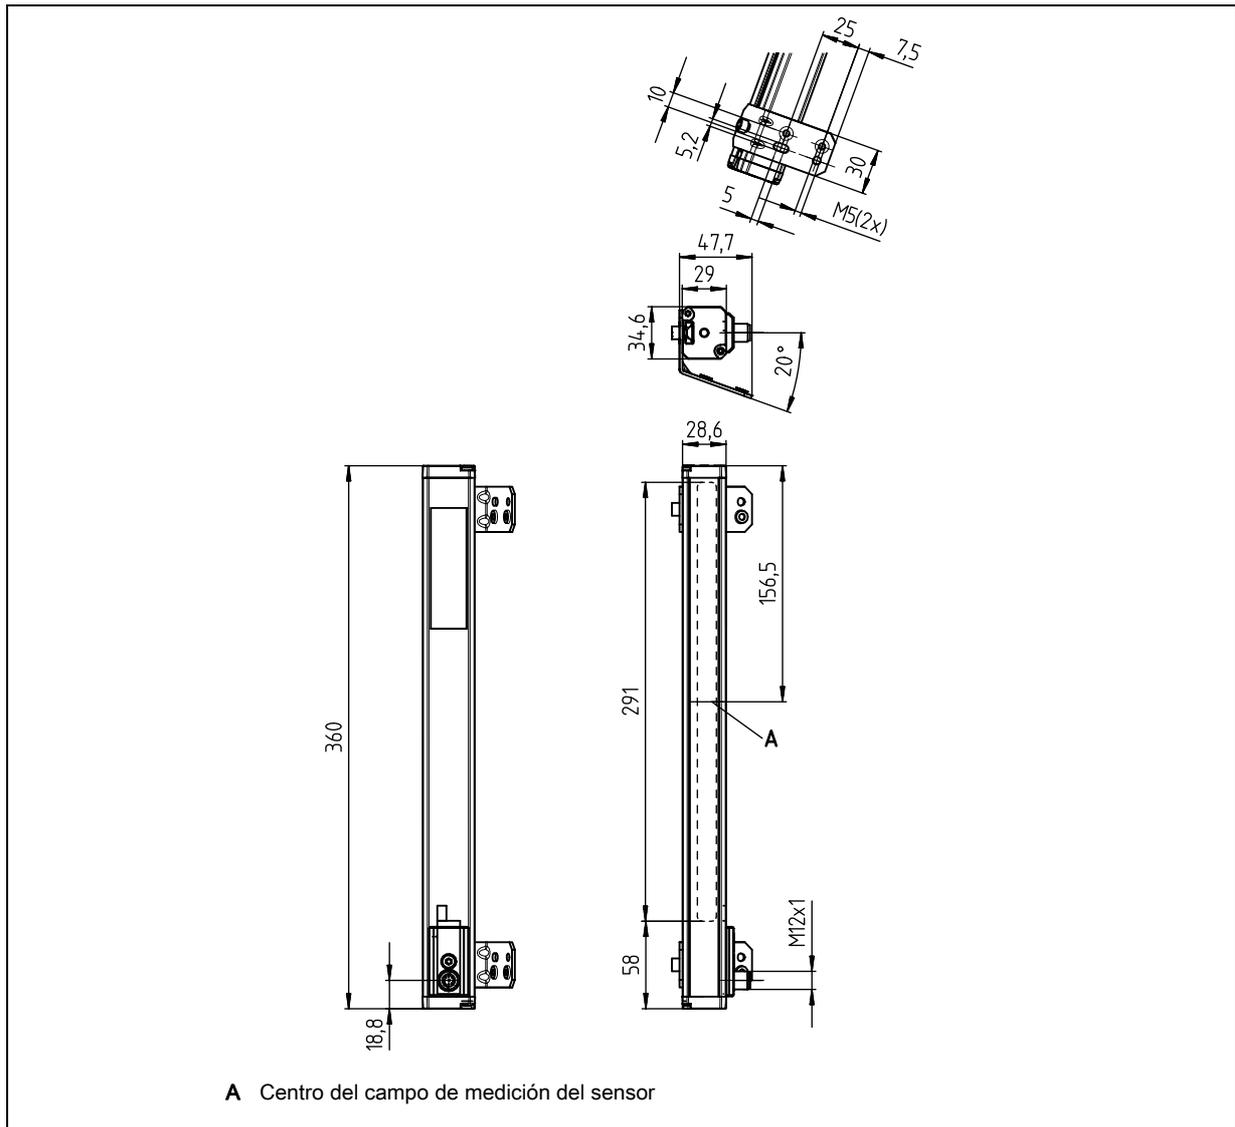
Dibujo acotado OGS 600-280/D...-M12.8 – Versión larga
